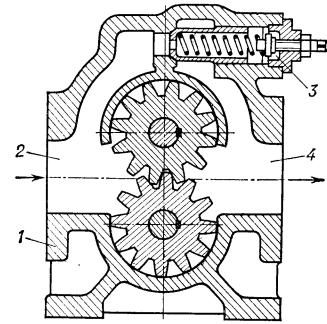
Зубчатый насос: 1 — корпус; 2 и 4 — отверстия для всасывания и нагнетания жидкости; 3 — предохранительный клапан.
